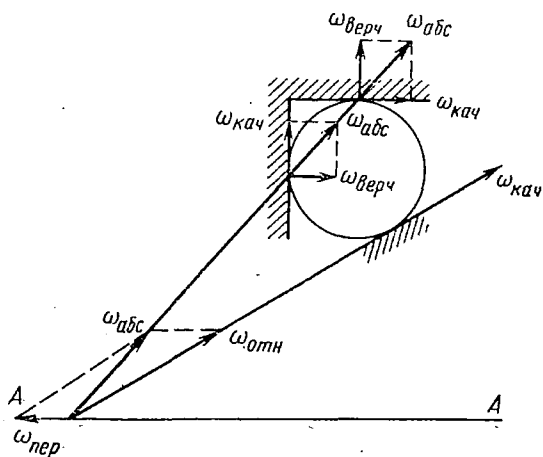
Кинематика прямоугольного шарикоподшипника:
